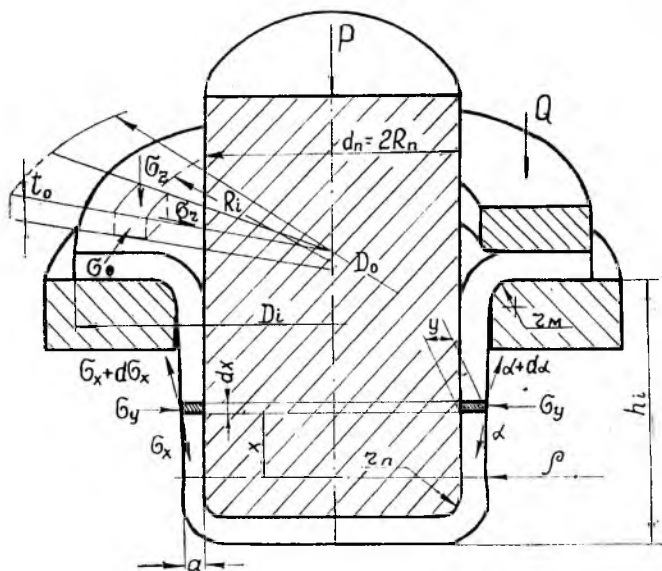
Принципиальная схема вытяжки цилиндрической детали
